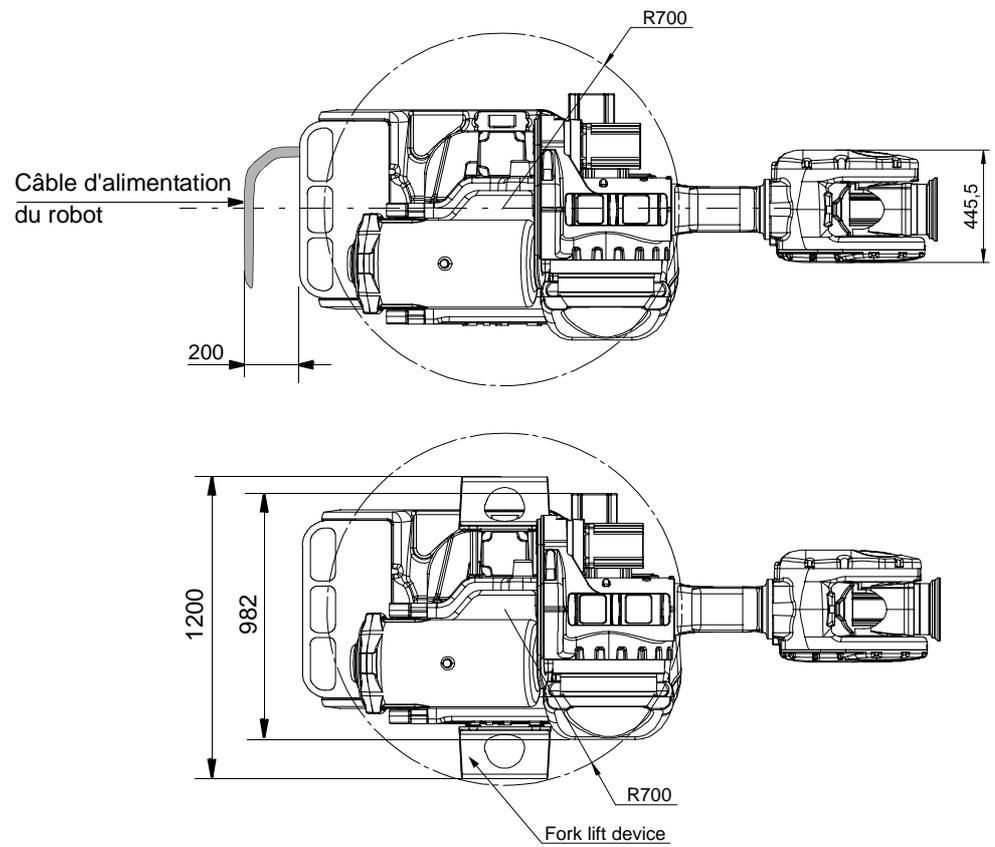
Vue du dessus du manipulateur (dimensions en mm)
